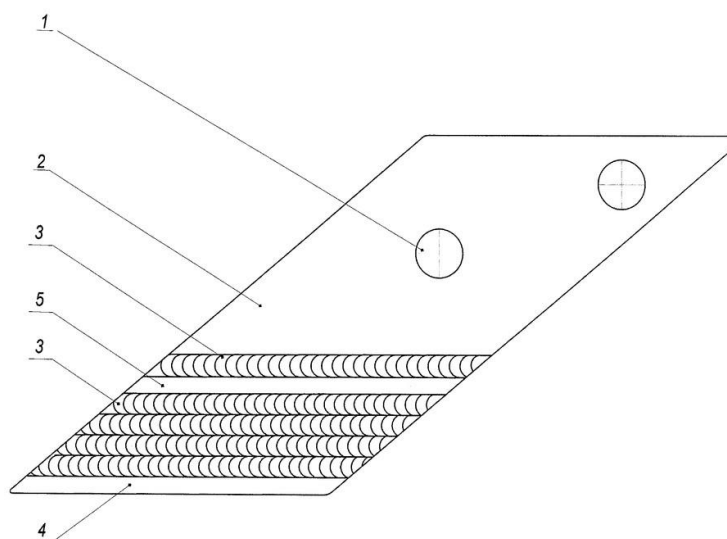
Восстановленное долото плужного лемеха (1 - присоединительный элемент; 2 – отверстия; 3 – Лезвийно-режущая часть; 4 – сварочный шов; 5 – износостойкое покрытие)
